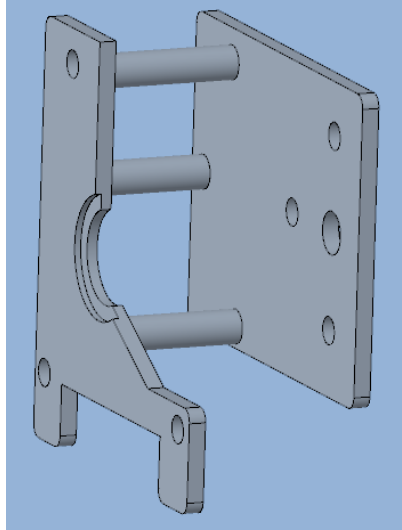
Estrutura de fixação do suporte para a perna asm001 e montagem_lateral1
